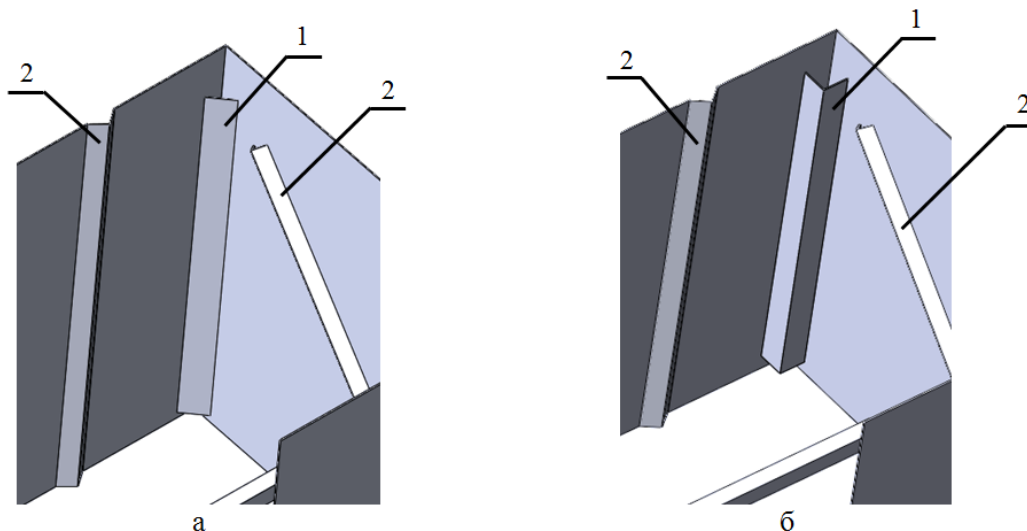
Фрагмент углового сварного соединения боковой и задней стенок цистерны:
